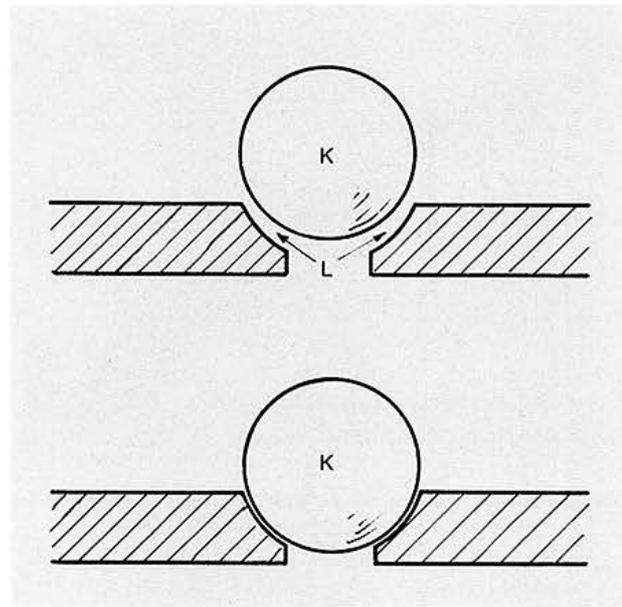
Kugelventil, oben geöffnet, unten geschlossen:
